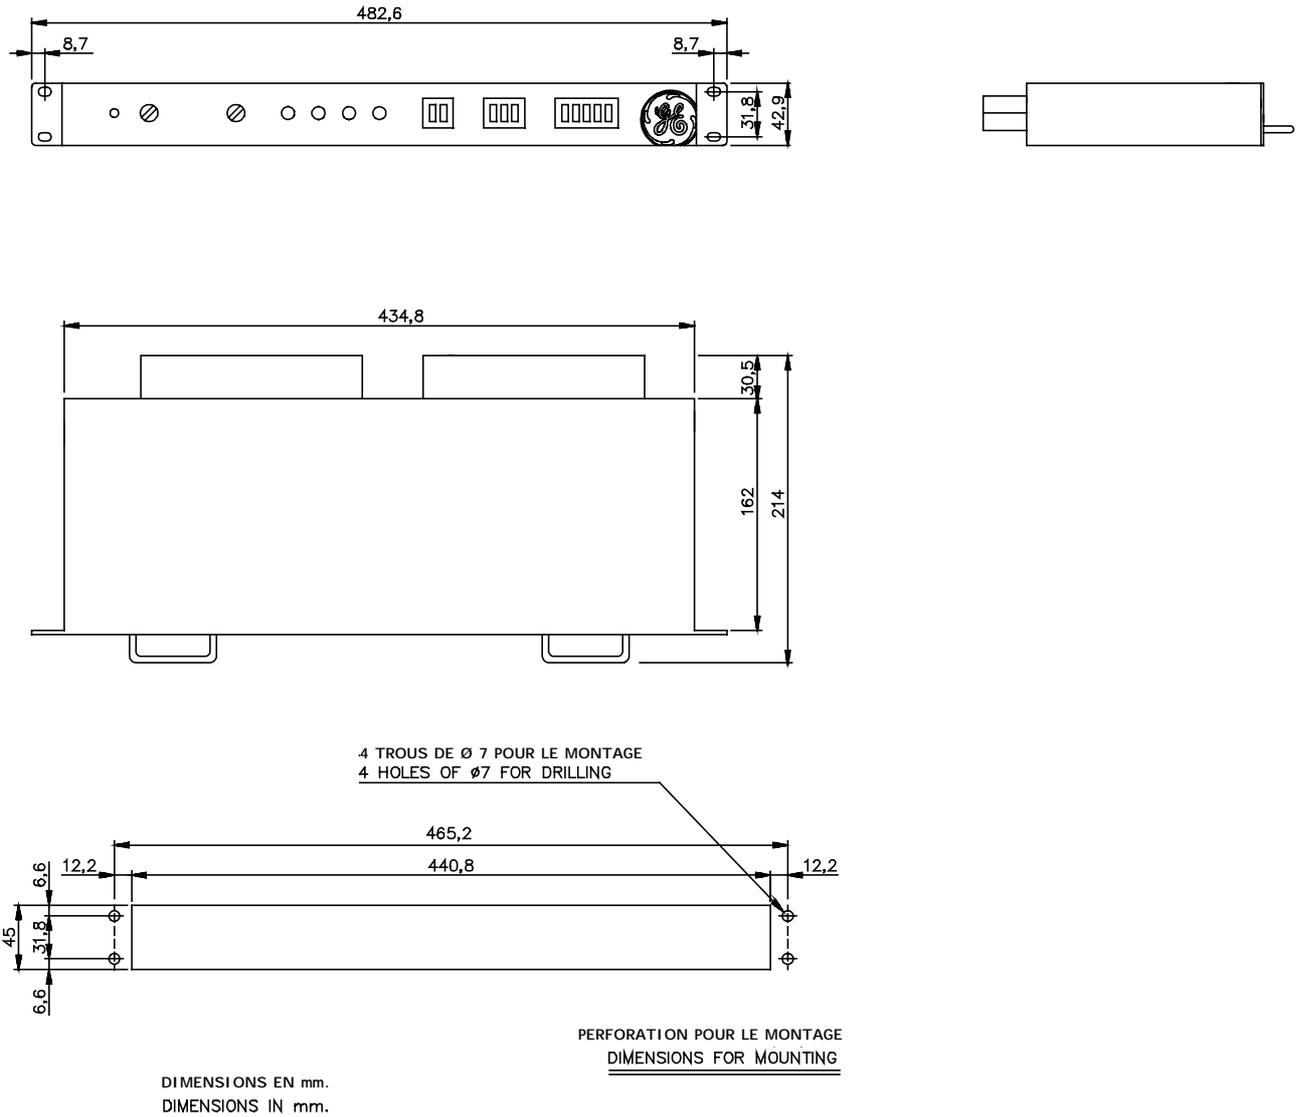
DIMENSIONS MECANQUES ET PLAN D'ALEPAGE (226B6086H11)
